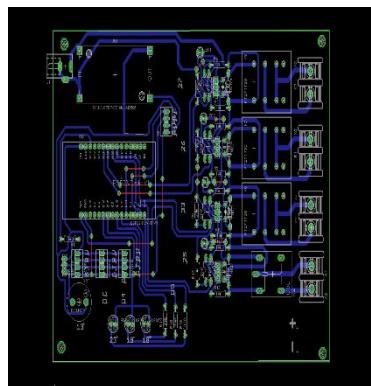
Design PCB Board hardware Mikrokontroller ESP32
